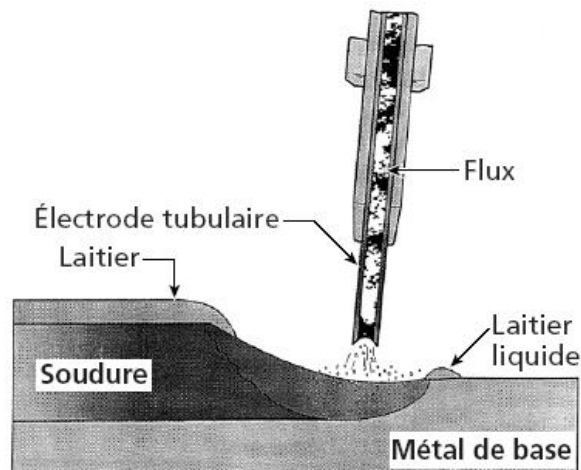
Soudage avec fil fourré autoprotégé
